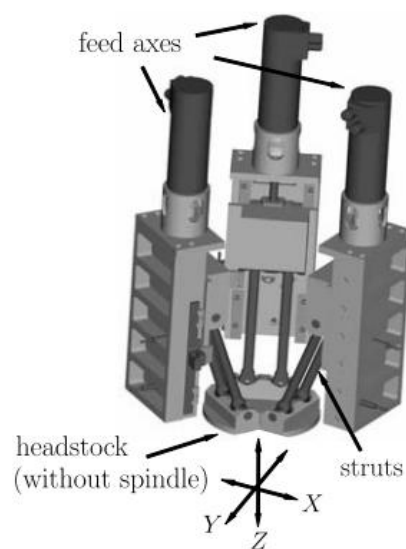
Werkzeugmaschinen mit Parallelkinematik¹⁰⁵
